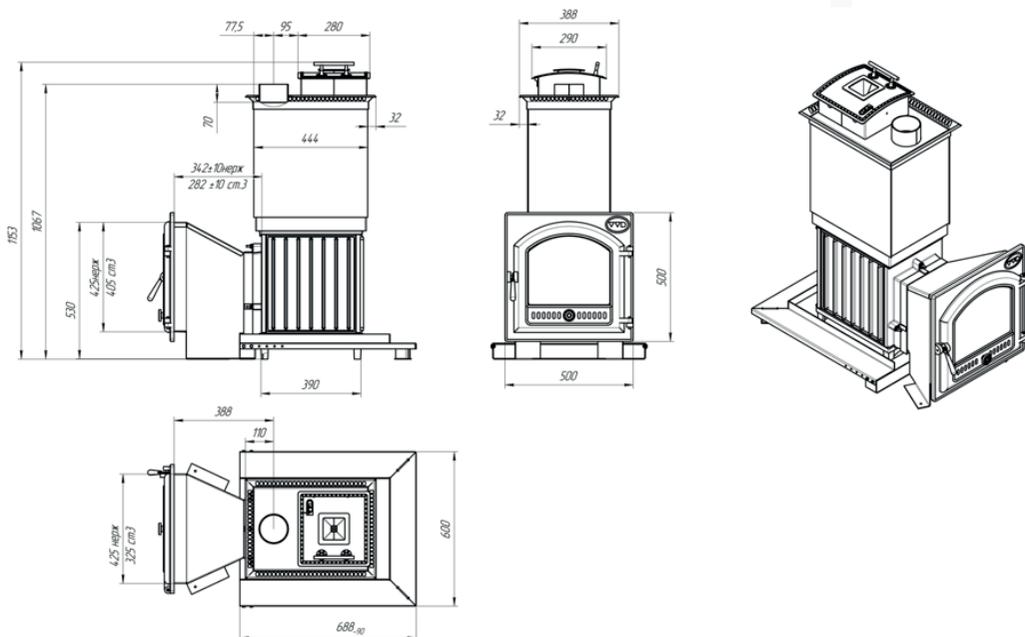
Топочный агрегат для бани Сударушка Семейная
